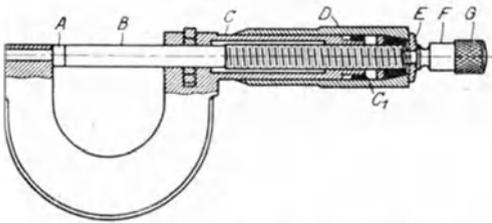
Mikrometer mit Gefühlschraube. Hommelwerke, Mannheim.
